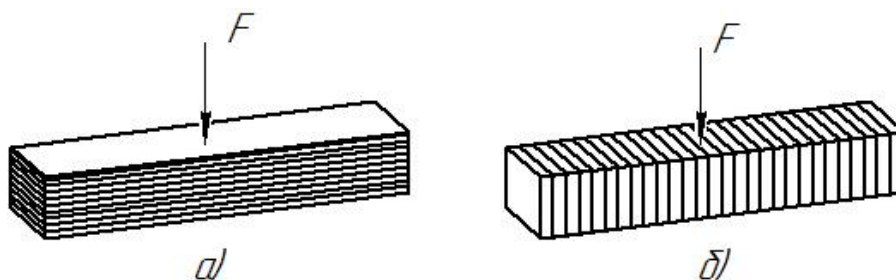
Схема FDM- печати заготовки для испытаний на срез:
